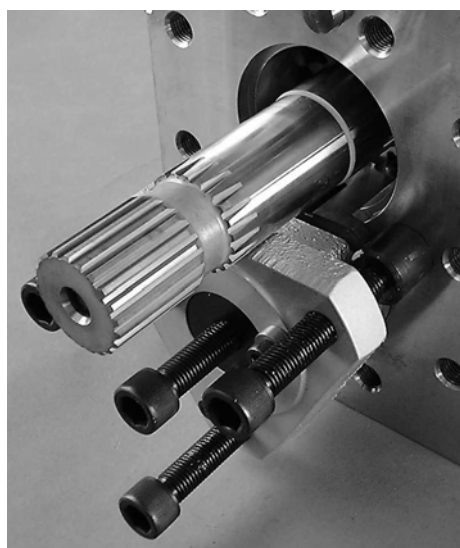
Съемник для подшипника, привинченный на стороне ASU
